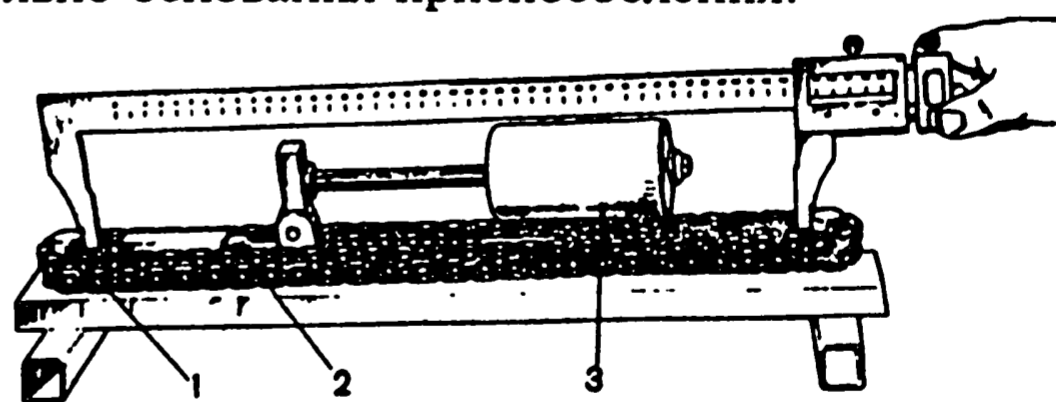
Приспособление 67.7824.9521 для проверки износа (вытяжки) цепи: 1 - ролик; 2 - регулировочная гайка; 3 - противовес
